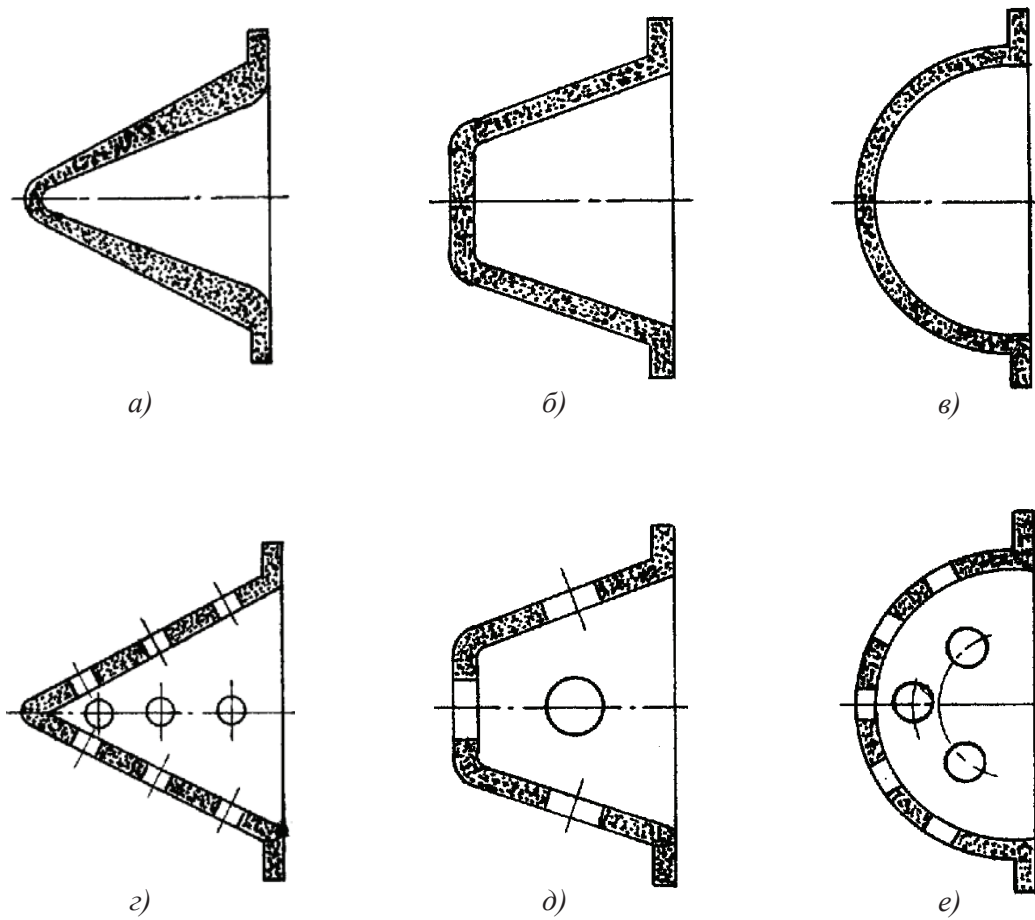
Различные варианты конструктивного исполнения диафрагмы (a...e) газосборного ресивера из пористой звукопоглощающей газопродуваемой структуры типа прессованного сетчатого материала (ПСМ), металлорезины (МР)
